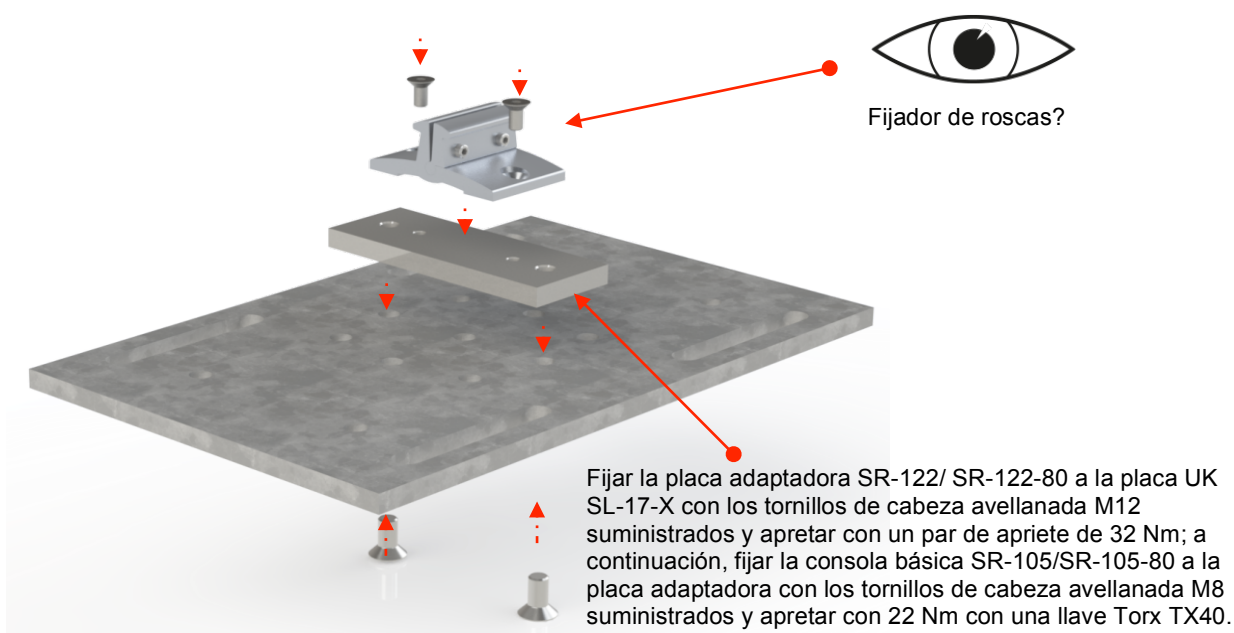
Montaje de la consola básica SR-105 en la placa adaptadora SR-122/ para placas UK SR-017
